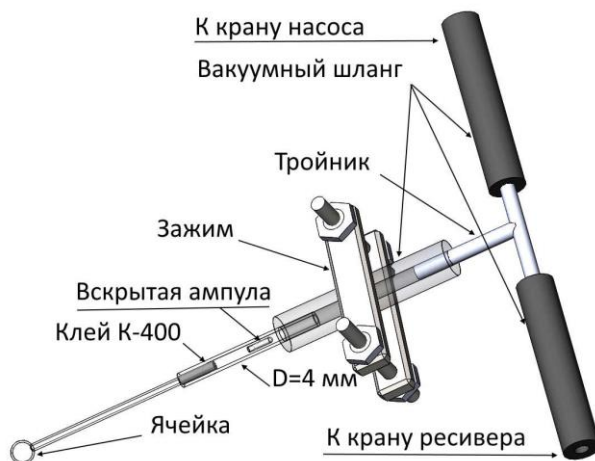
Основные элементы и приспособления при изготовлении ячейки
